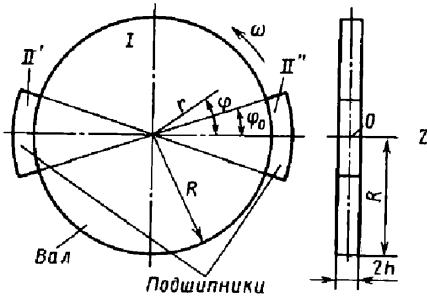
Схема металлополимерной трибосистемы вал – частичный подшипник
